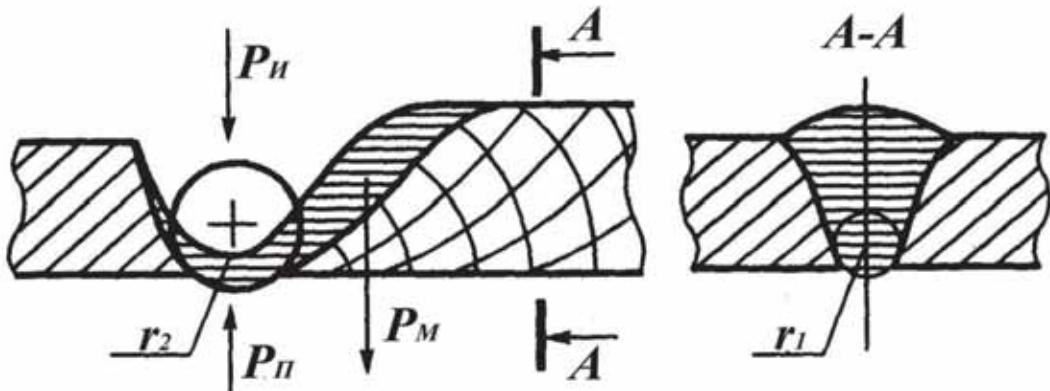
Схема формирования проплавления сварного шва:
